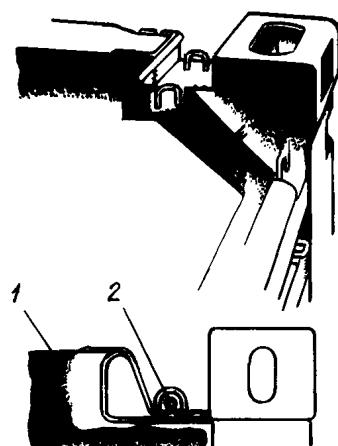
Устройство для крепления чехла к углам контейнера:
